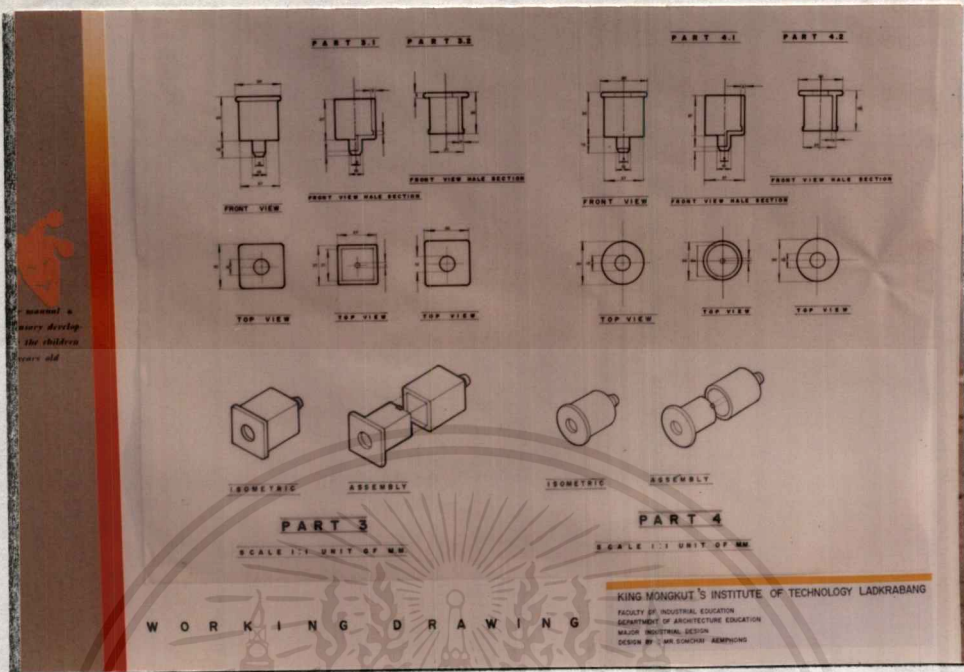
แบบนำเสนอ WORKING DRAWING 1
